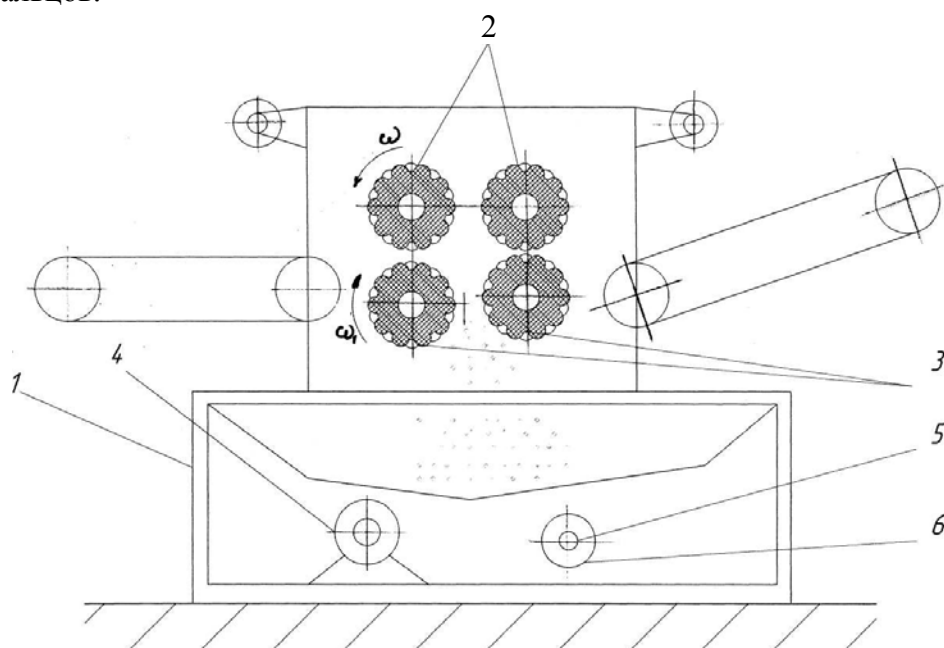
Технологическая схема молотильного аппарата роторно-винтового типа 1 – рама; 2, 3 – верхняя и нижняя пара обмолачивающих вальцов; 4 – электродвигатель; 5 – промежуточный вал; 6 – вариатор
